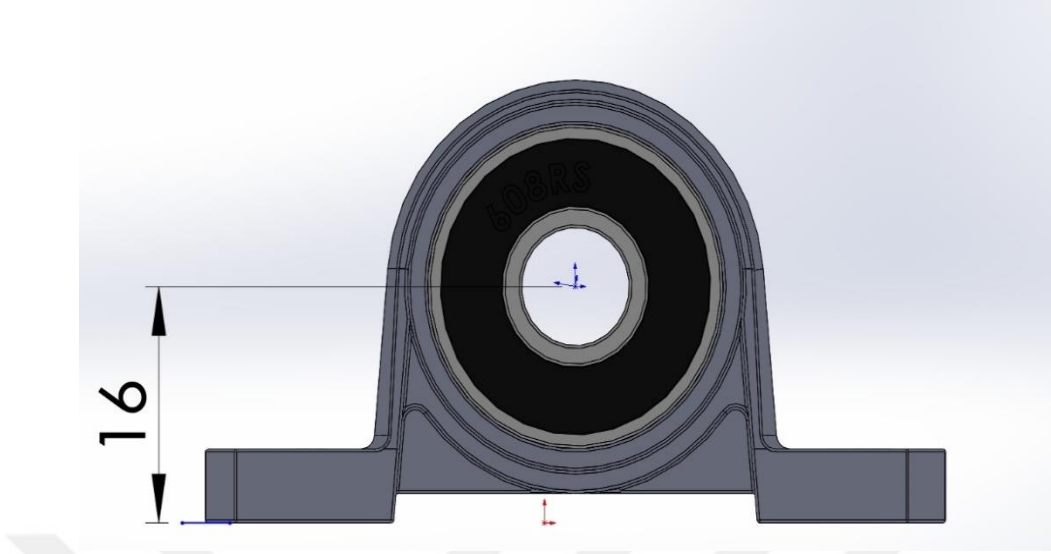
Motor ve Encoder Yatakları 3D Simplify görünümü
